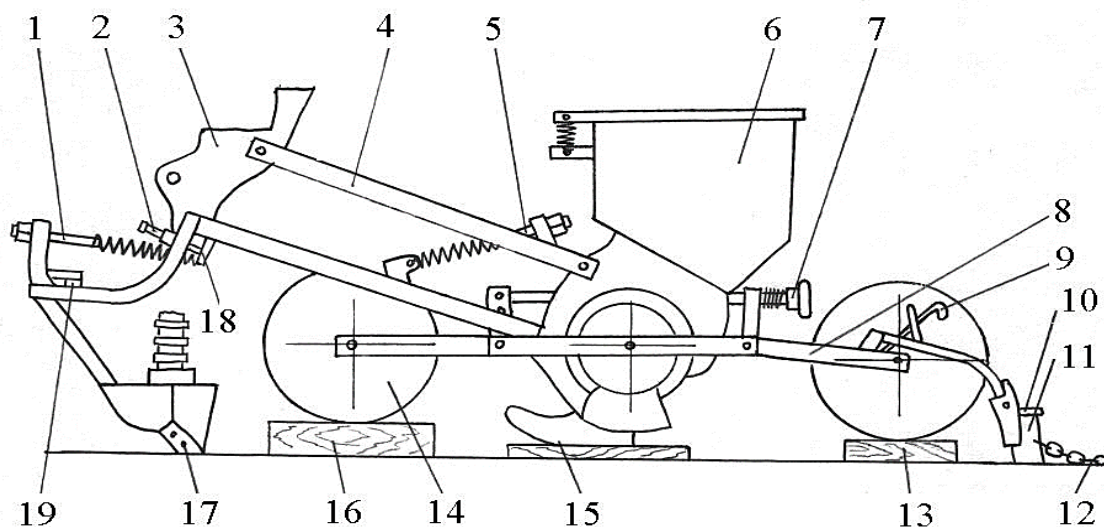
Схема установки глубины хода сошников сівалки ССТ – 12Б:
